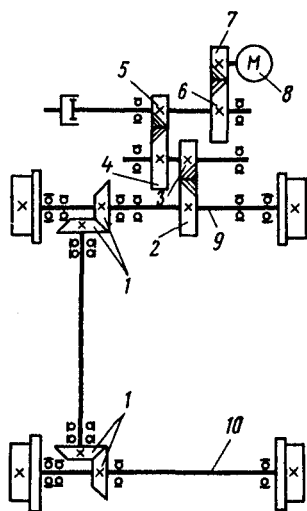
Кинематическая схема привода манипулятора ПРТ8-2Д:
